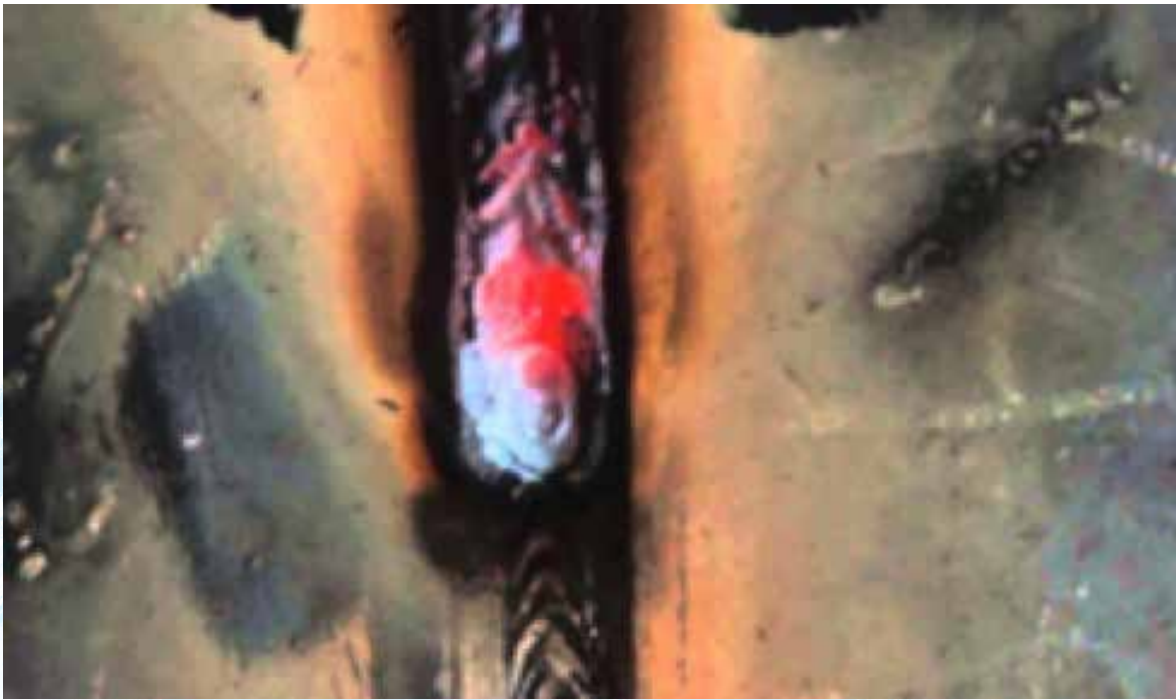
Estructura de la zona fundida en una soldadura con llama oxiacetilénica (500X)
